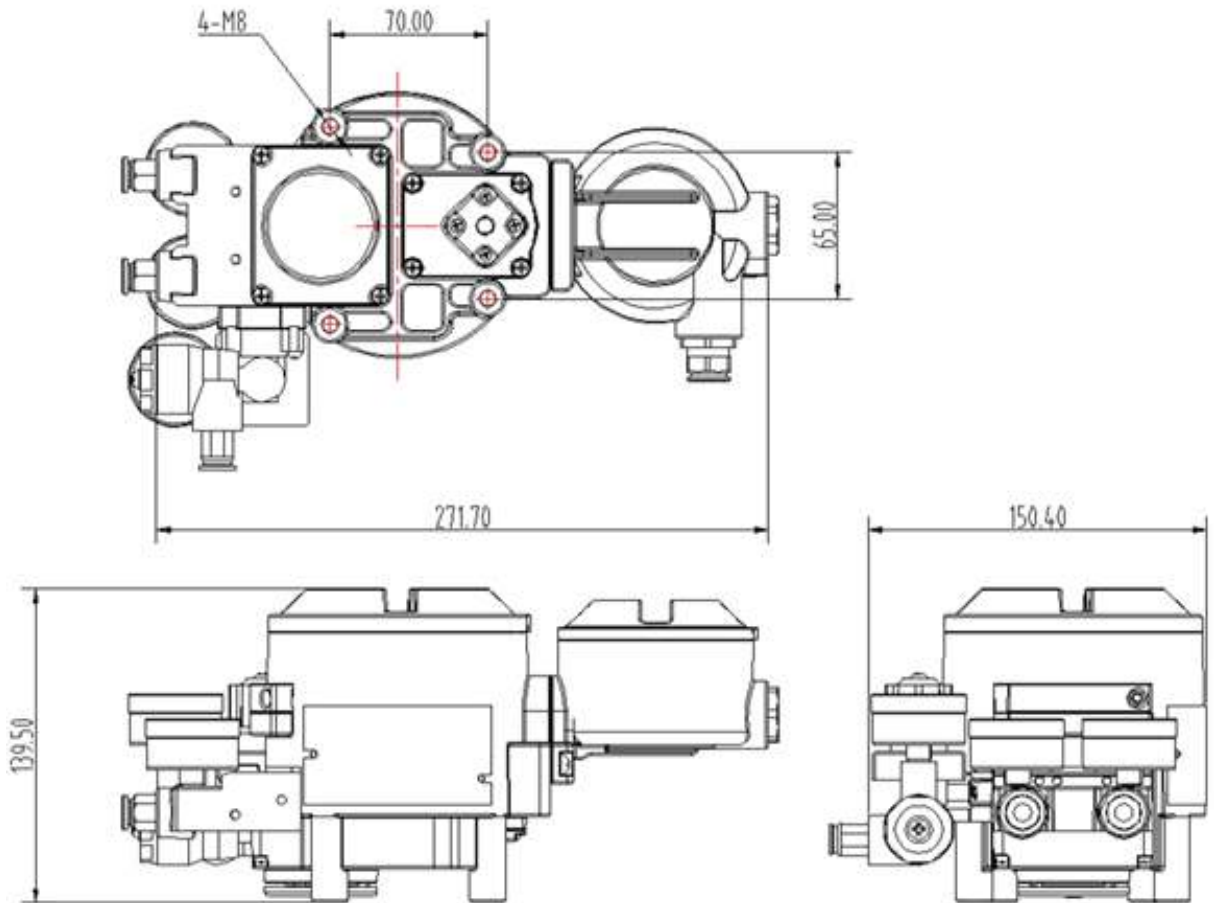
GK-2300/2500 系列智能阀门定位器外形尺寸图
